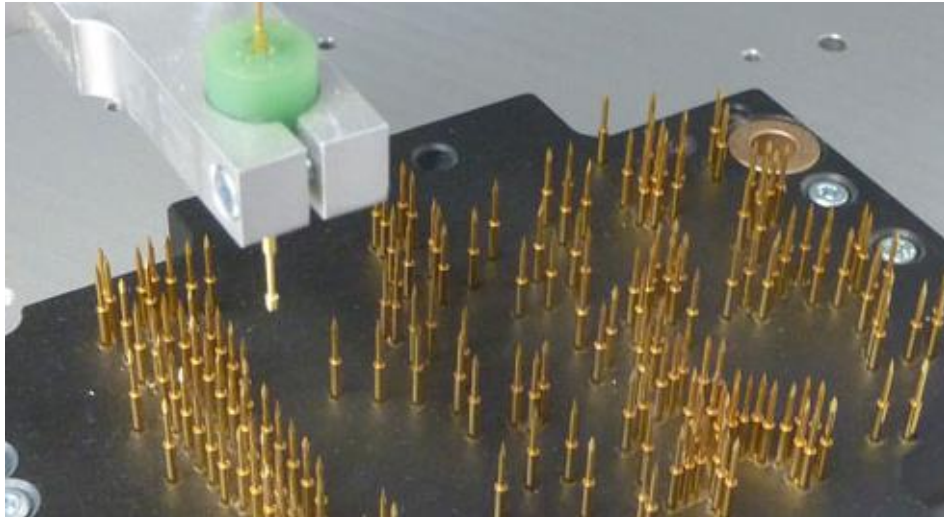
Exemplo de placa de cama de agulhas personalizada com as agulhas já fixadas (An overview of PCB testing and inspection methods, s.d.).
